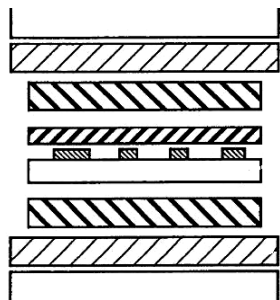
Резина для амортизирующей прокладки горячего прессования, способ изготовления этой амортизирующей прокладки горячего прессования и способ изготовления печатной платы
